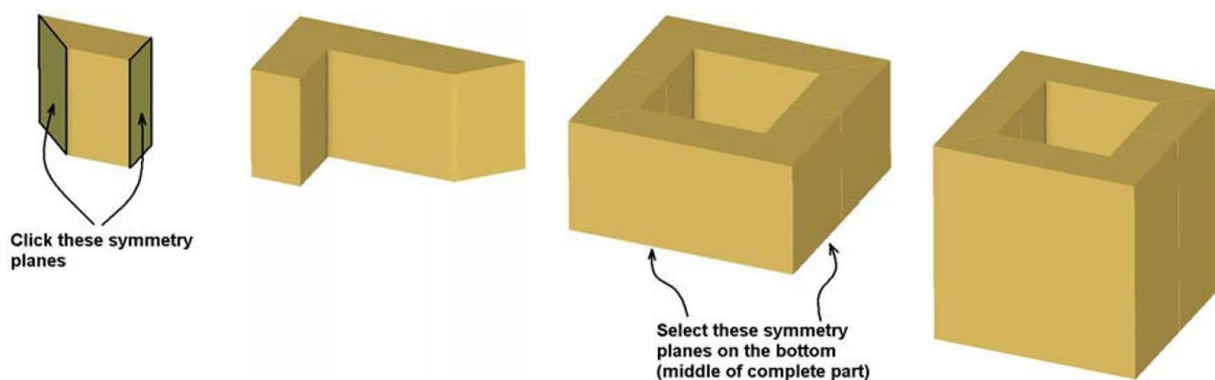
Схема моделювання 1/16 частини заготовки
